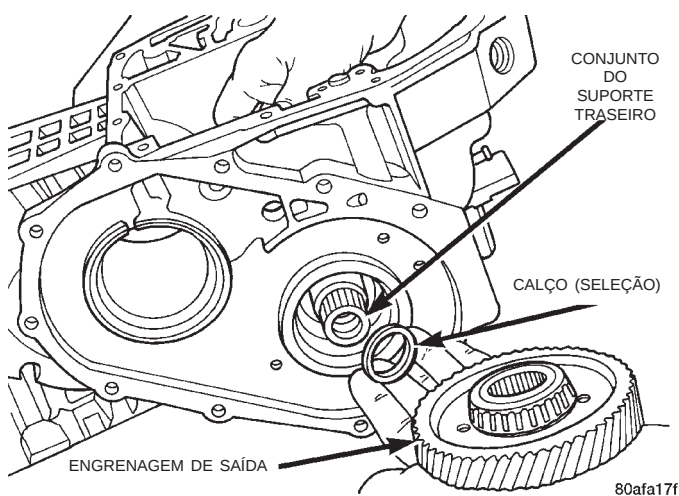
Engrenagem de Saída e Calço (Seleção)
